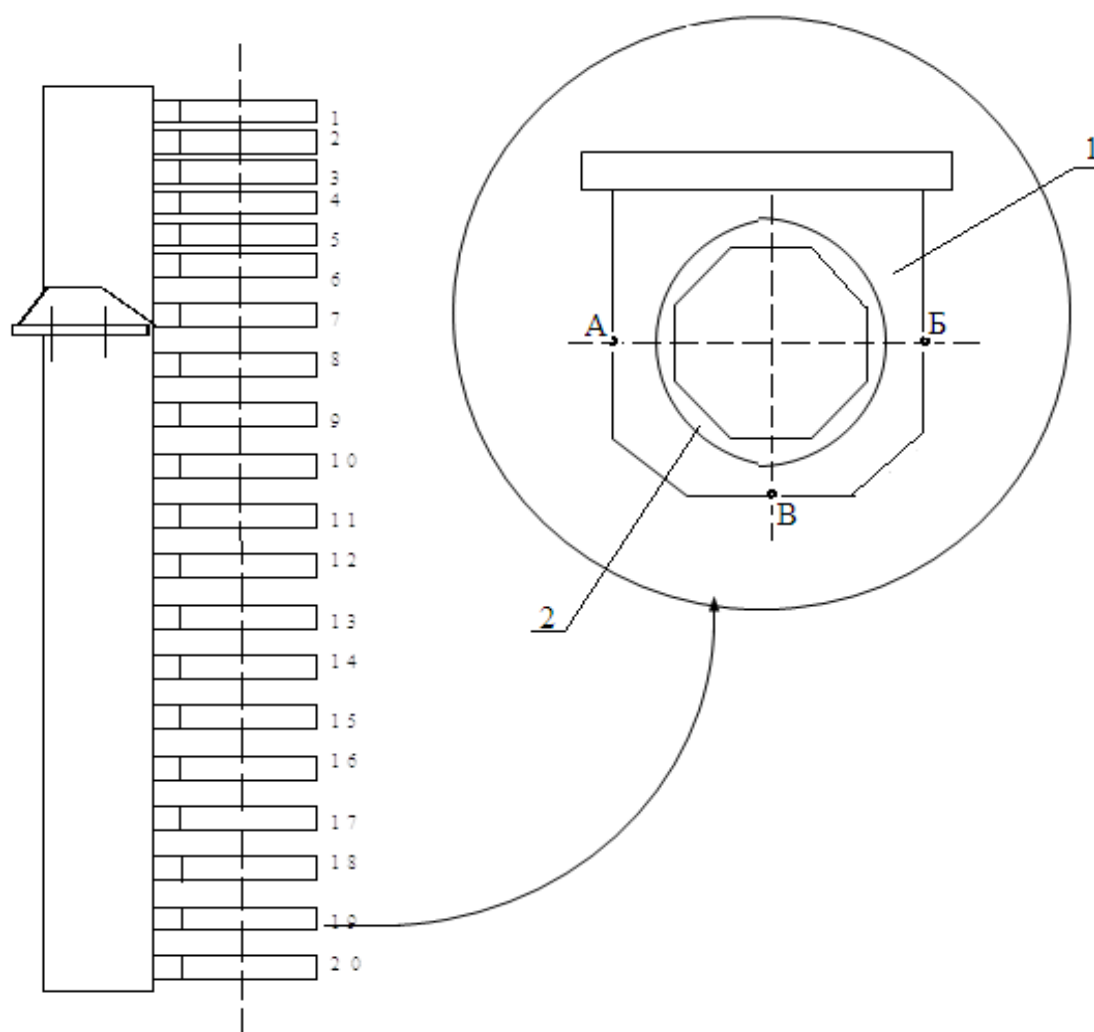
Схема устройства стапеля (1 – стальная консоль; 2 – пластиковая вставка с центральным отверстием правильной шестигранной формы) [Berth layout (1 – steel console; 2 – plastic insert with a central hole of regular hexagonal shape)]
